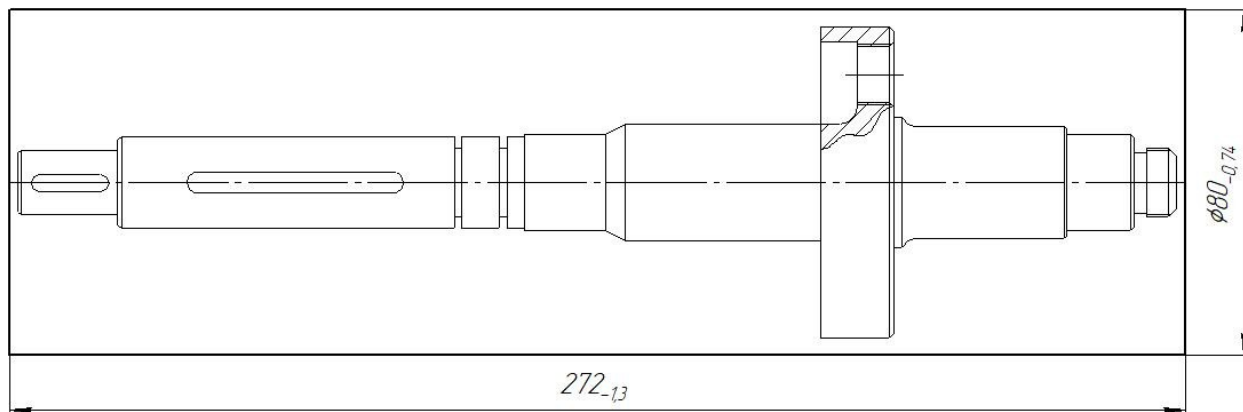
Заготовка детали «Фланцевый вал» из проката
